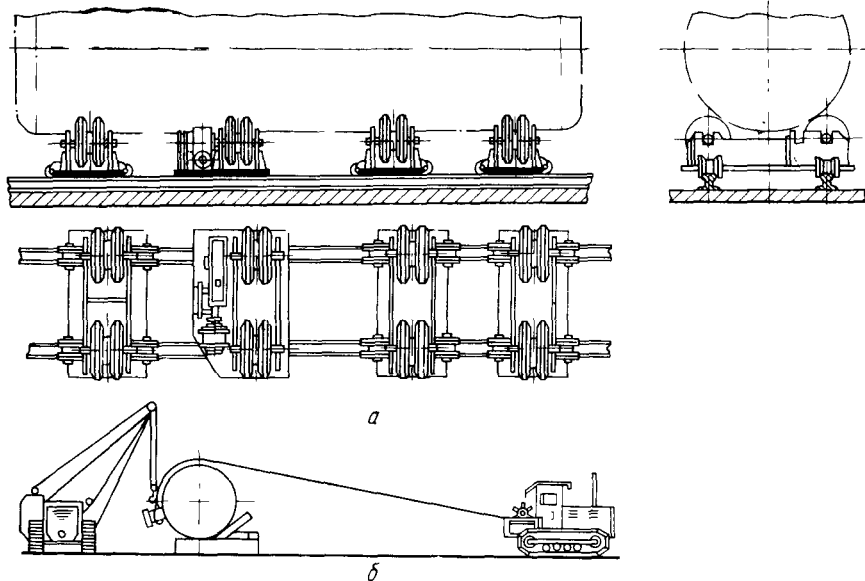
Стенды для сборки цилиндрических аппаратов:
